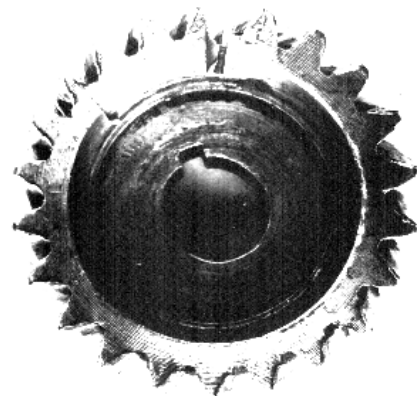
Ускоренный износ зубьев шестерни из стали 45 механизма привода насоса двигателя 4Ч10,5/13 из-за заниженной твердости
